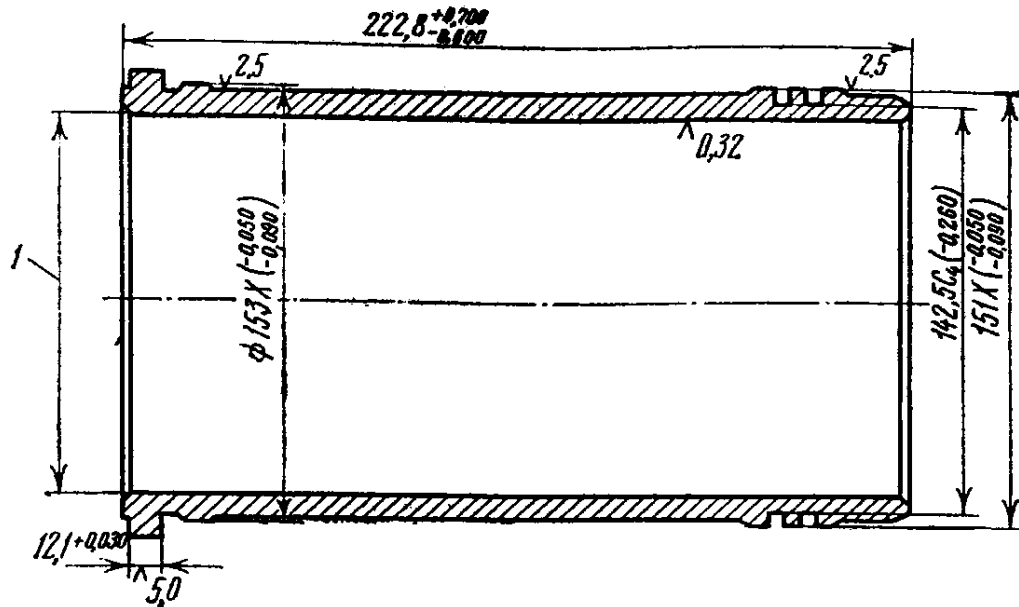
Робоче креслення гільзи циліндрів двигуна СМД-60
